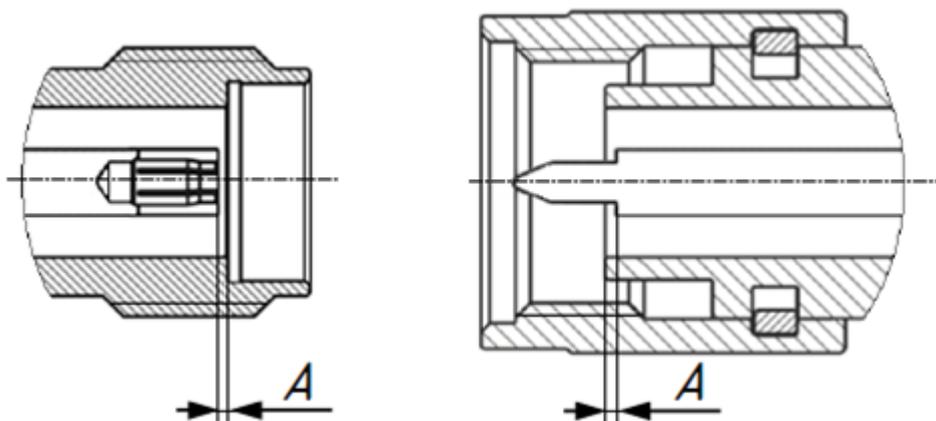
Соединители тип 3,5 мм (розетка слева, вилка справа)
